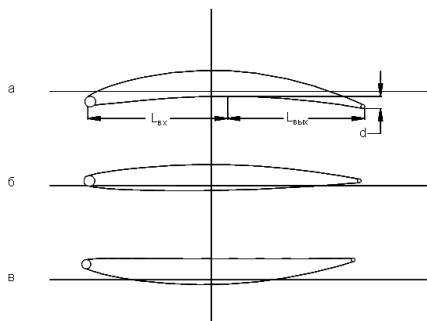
Форма кинематического профиля пера лопатки для случаев:
